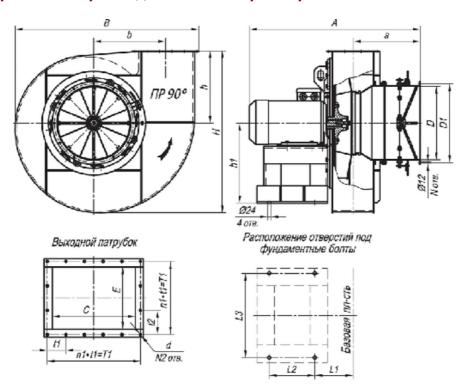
Габаритные и присоединительные размеры тягодутьевых машин типа ВДН и ДН №6,3-13 исп-1.
